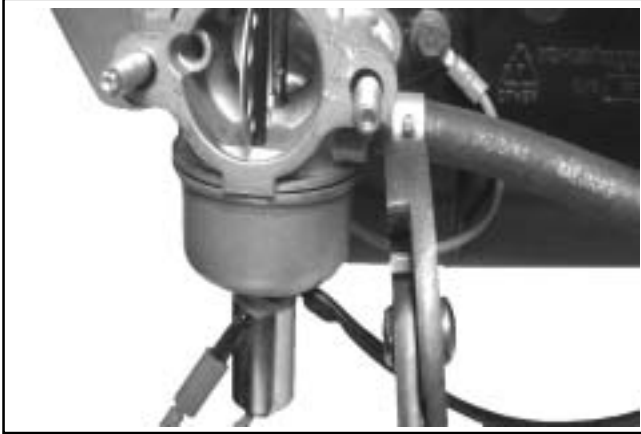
Desconexión de la tubería de combustible del carburador.
